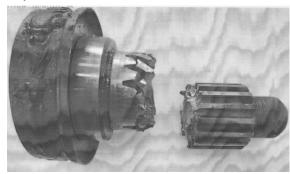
Промежуточная опора карданной передачи 650118-2205006-001: 1 — шлицевый конец; 2 — шариковый подшипник; 3 — резиновый виброизолятор; 4 — соединительный фланец
